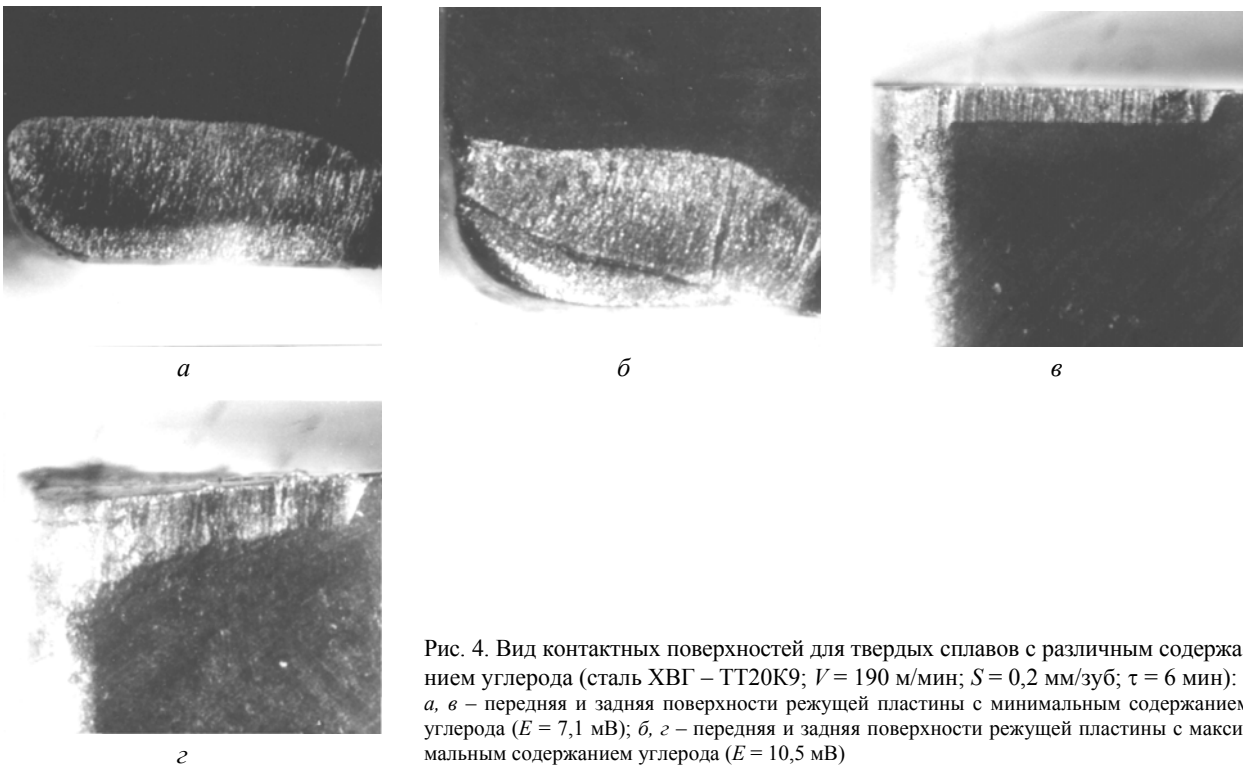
Вид контактных поверхностей для твердых сплавов с различным содержанием углерода (сталь ХВГ – ТТ20К9; $V = 190$ м/мин; $S = 0,2$ мм/зуб; $\tau = 6$ мин): а, в – передняя и задняя поверхности режущей пластины с минимальным содержанием углерода ($E = 7,1$ мВ); б, г – передняя и задняя поверхности режущей пластины с максимальным содержанием углерода ($E = 10,5$ мВ)
